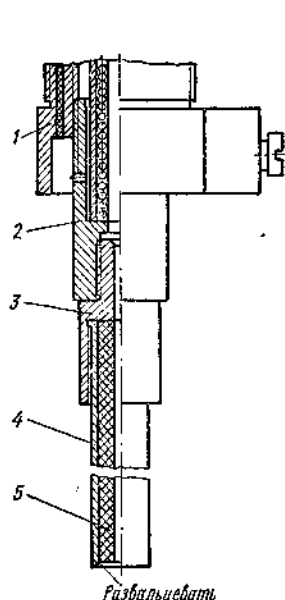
Схема опытной приставки к держателю для сварки с увеличенным вылетом электрода:
